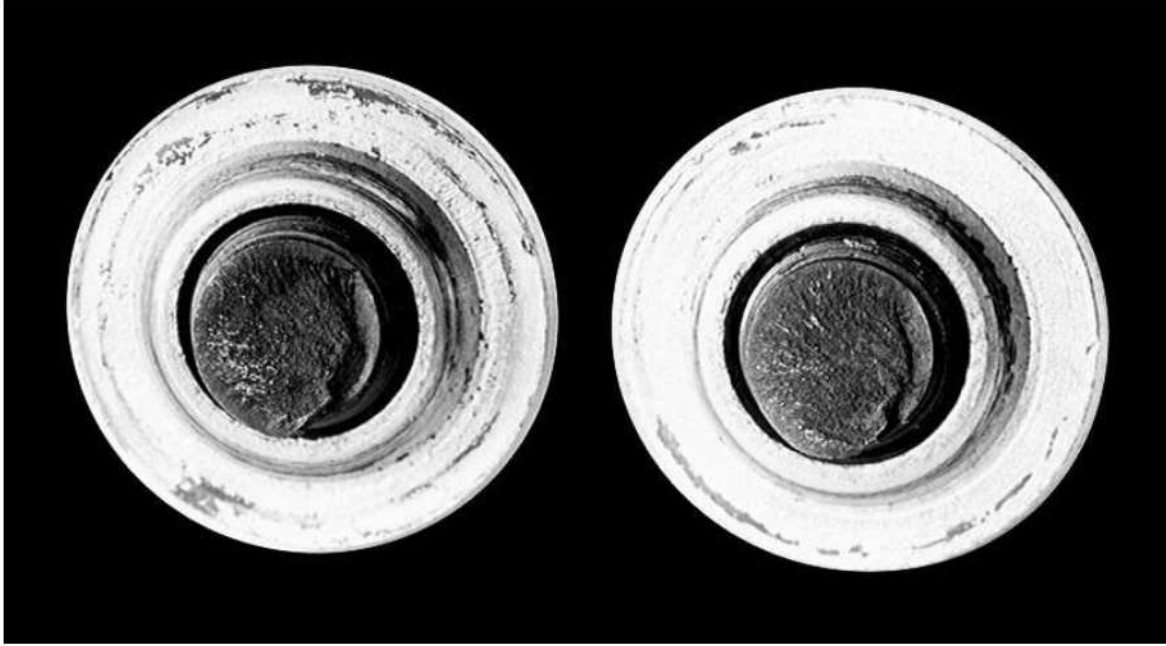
Aspecto de la fractura de los pernos rotos. Fractura de carácter frágil iniciada en el primer filete de la rosca.
